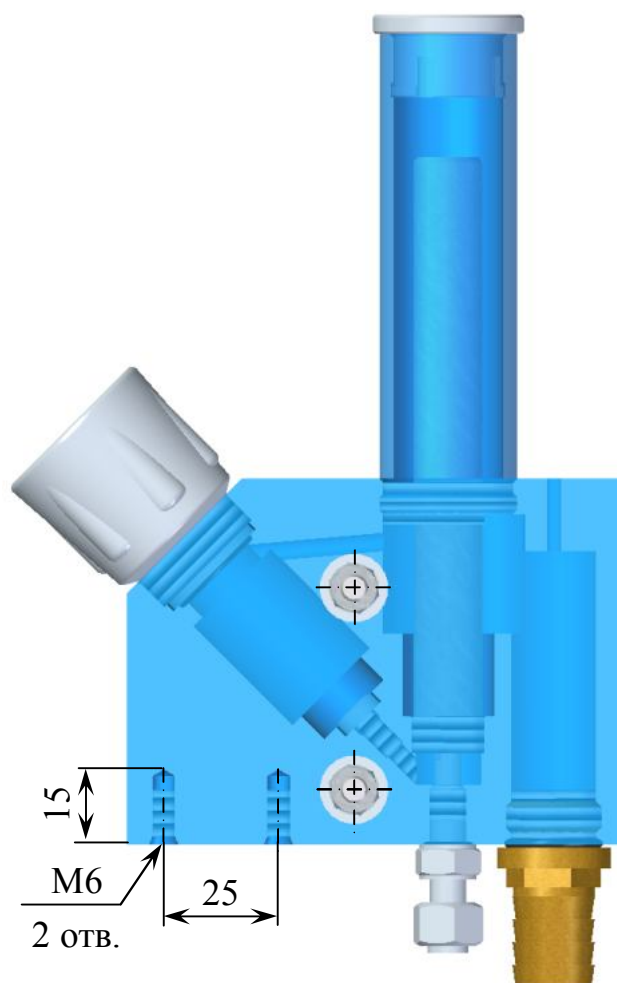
Присоединительные размеры модуля для крепления на горизонтальной поверхности
